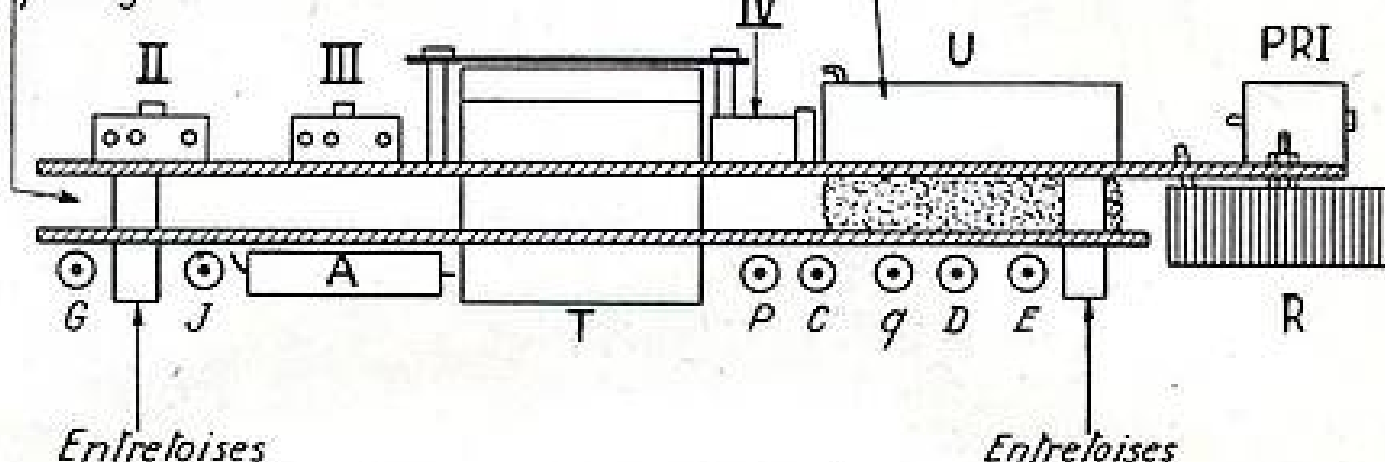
Vue en coupe des deux plaquettes assemblées
